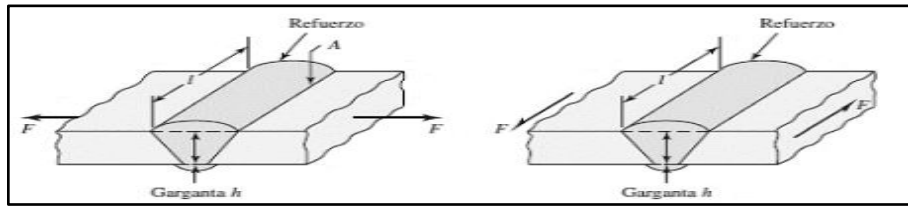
Cargas en la soldadura. Fuente: (Budynas & Nisbett, 2008, pág. 460)
